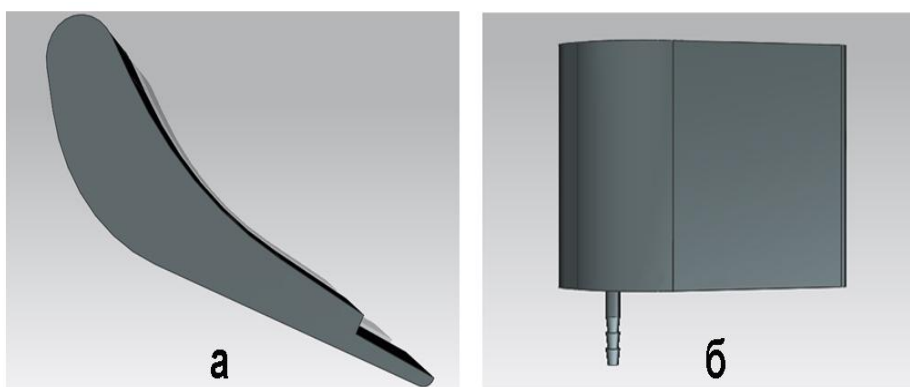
Модель лопатки: а – вид сверху; б – вид сбоку
